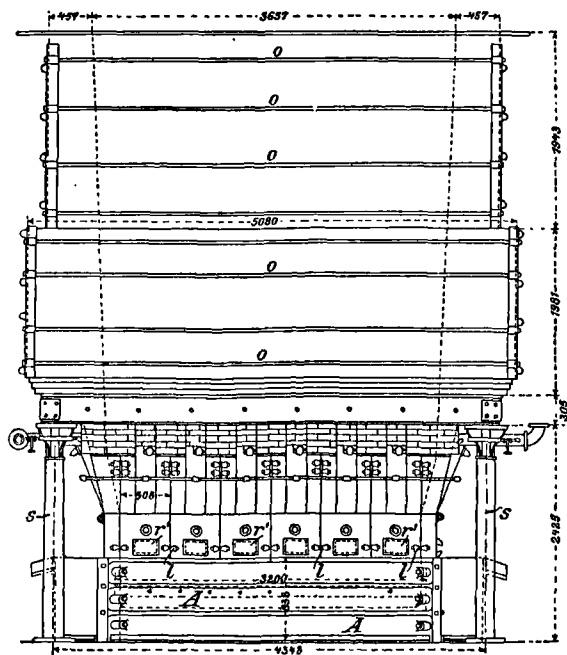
Four américain des Globe Smelting works; vue extérieure.
